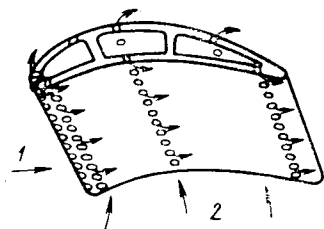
Схема лопатки с пленочным охлаждением: 1—поток горячего газа; 2—охлаждающий воздух [26]
